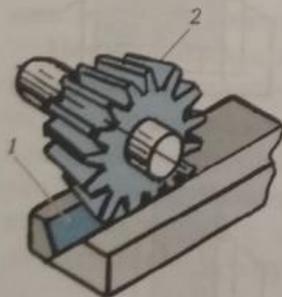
Обработка наклонной поверхности угловой фрезой:
